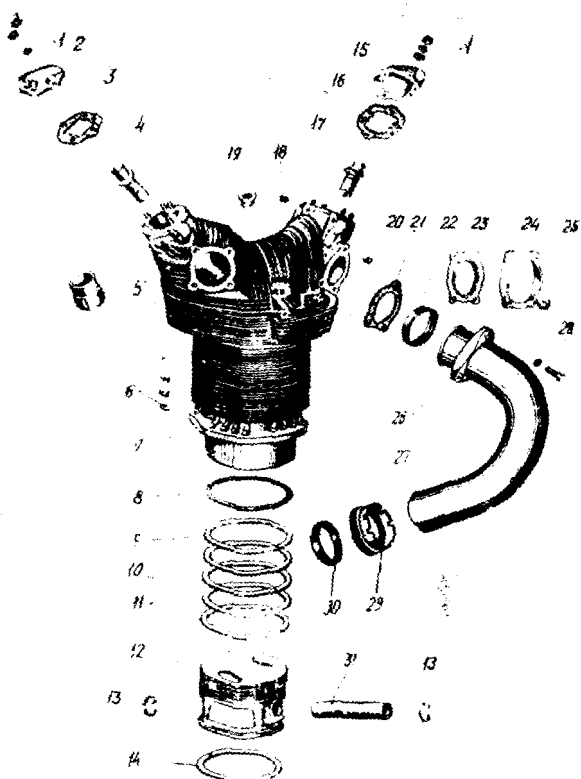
Детали цилиндра и поршня: 1—гайка, шайба и шайба Гровера для крепления крышки рычага клапана; 2—крышка рычага клапана выпуска; 3—прокладка; 4—направляющая клапана выпуска; 5—штуцер кожуха тяги; 6—гайка, шайба и контргайка крепления цилиндра; 7—цилиндр; 8—маслоуплотнительное кольцо цилиндра; 9, 10—газоуплотнительные поршневые кольца; 11—маслосбрасывающие кольца; 12—поршень; 13—замок поршневого пальца; 14—маслосборное кольцо; 15—крышка рычага клапана впуска; 16—прокладки; 17—направляющая клапана впуска; 18—втулка для крепления дефлектора; 19—втулка свечи; 20—втулка для винта крепления фланца выпускной трубы; 21—прокладка; 22—уплотнительное кольцо; 23—прокладка; 24—фланец выпускной трубы; 25—гайка; 26—фланец впускной трубы; 27—впускная труба; 28—болт и шайба; 29—гайка уплотнения впускной трубы; 30—уплотнительное кольцо; 31—палец поршня
